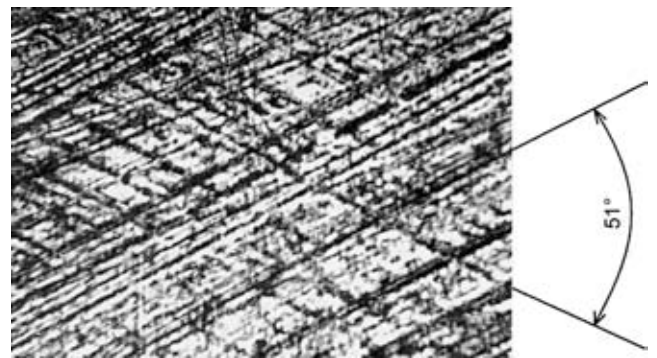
Поверхность образца, обработанного брусками АСВ 80/63 М1 100 %
